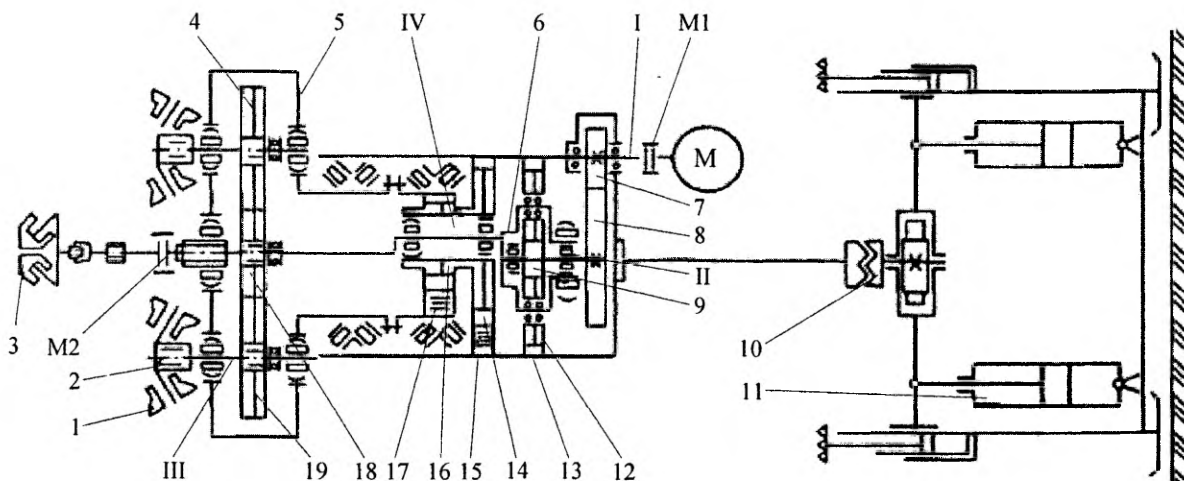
Кинематическая схема бурового станка «Стрела-77» [6]
